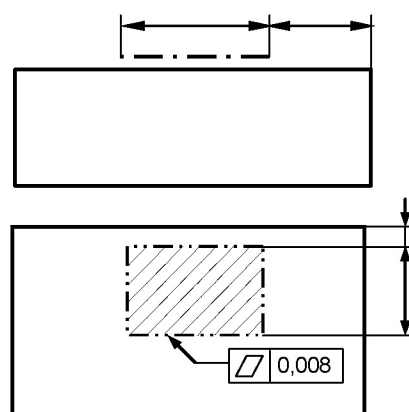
Indicación de posición de la zona de tolerancia en vista frontal
